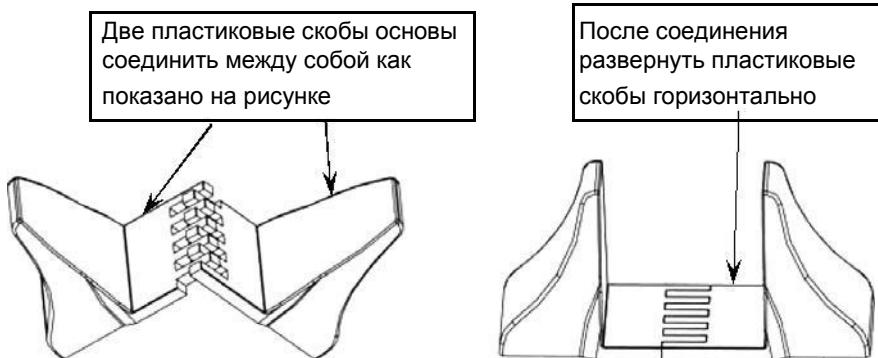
Сборка пластиковых основ для вертикальной установки изделия
